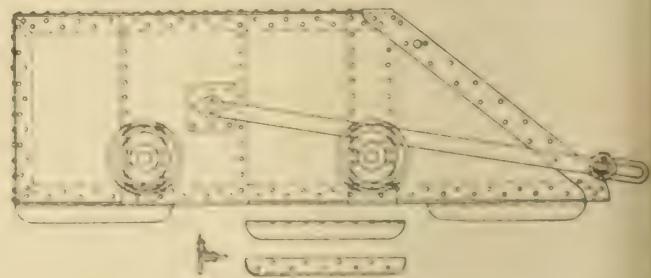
Skip der Quincy-Grube, Aufsicht.
